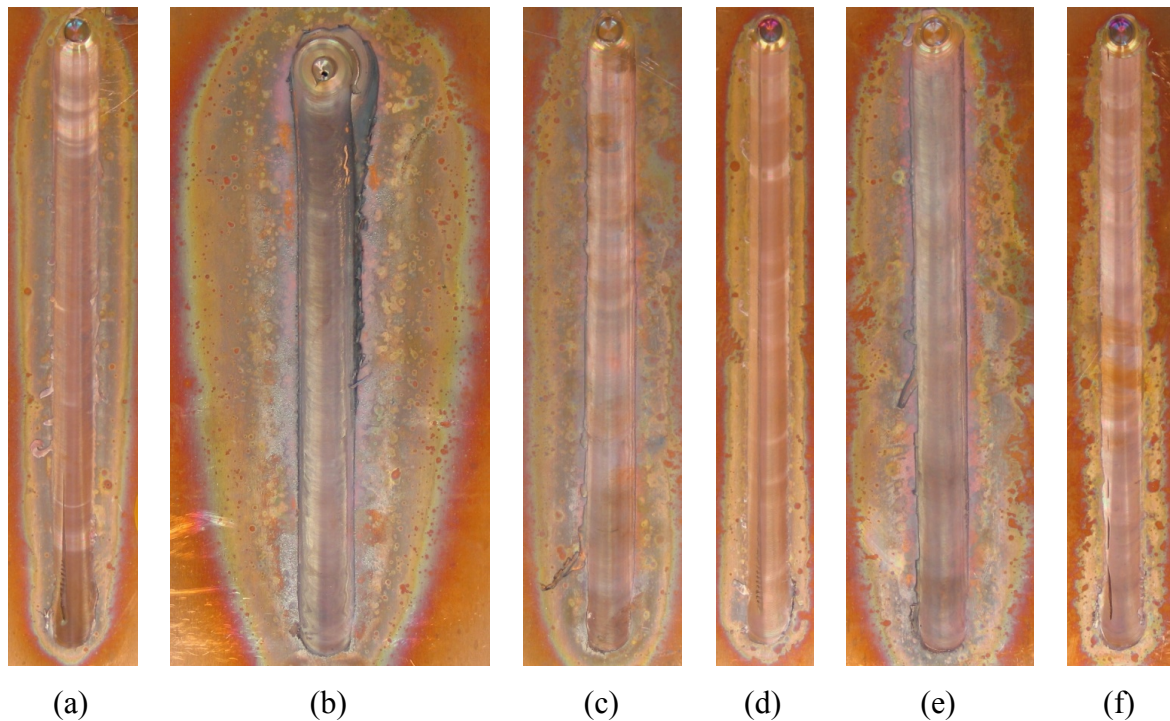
Aspecto superficial das soldaduras obtidas: (a) *CuW7.5V20*; (b) *CuW10V10*; (c) *CuW10V20*; (d) *CuW10V40*; (e) *CuW12.5V20*; (f) *CuW12.5V40*.
